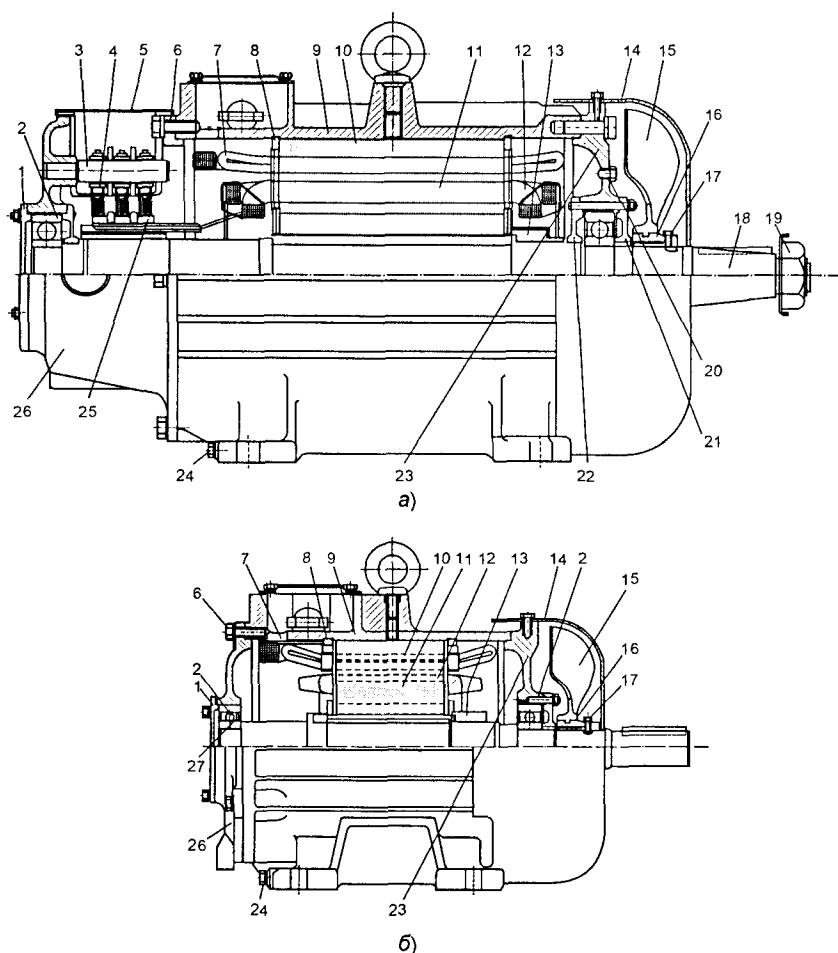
Крановые асинхронные электродвигатели: а — МТ 41 с фазным ротором, б — МТК-11 с короткозамкнутым ротором; 1, 21 и 22 — крышки подшипниковых камер; 2 — подшипник; 3 — палец щеткодержателя; 4 — щеткодержатель; 5 — крышка окна в подшипниковом щите; 6 — болт крепления подшипникового щита; 7 — двухслойная обмотка статора; 8 — запорное кольцо сердечника; 9 — корпус статора; 10 — сердечник статора; 11 — сердечник ротора; 12 — обмотка ротора; 13 — втулка на валу, прижимающая сердечник ротора; 14 — кожух вентилятора; 15 — литой алюминиевый вентилятор; 16 — стальная втулка залитая в вентилятор; 17 — стопорный винт крепления вентилятора; 18 — конический рабочий конец вала со шпонкой; 19 — затяжная гайка; 20 — болт, закрывающий отверстие в подшипниковом щите для измерения воздушного зазора между статором и ротором; 23 и 26 — подшипниковые щиты; 24 — болт для присоединения заземления; 25 — контактные кольца; 27 — защитная шайба шарикоподшипников
